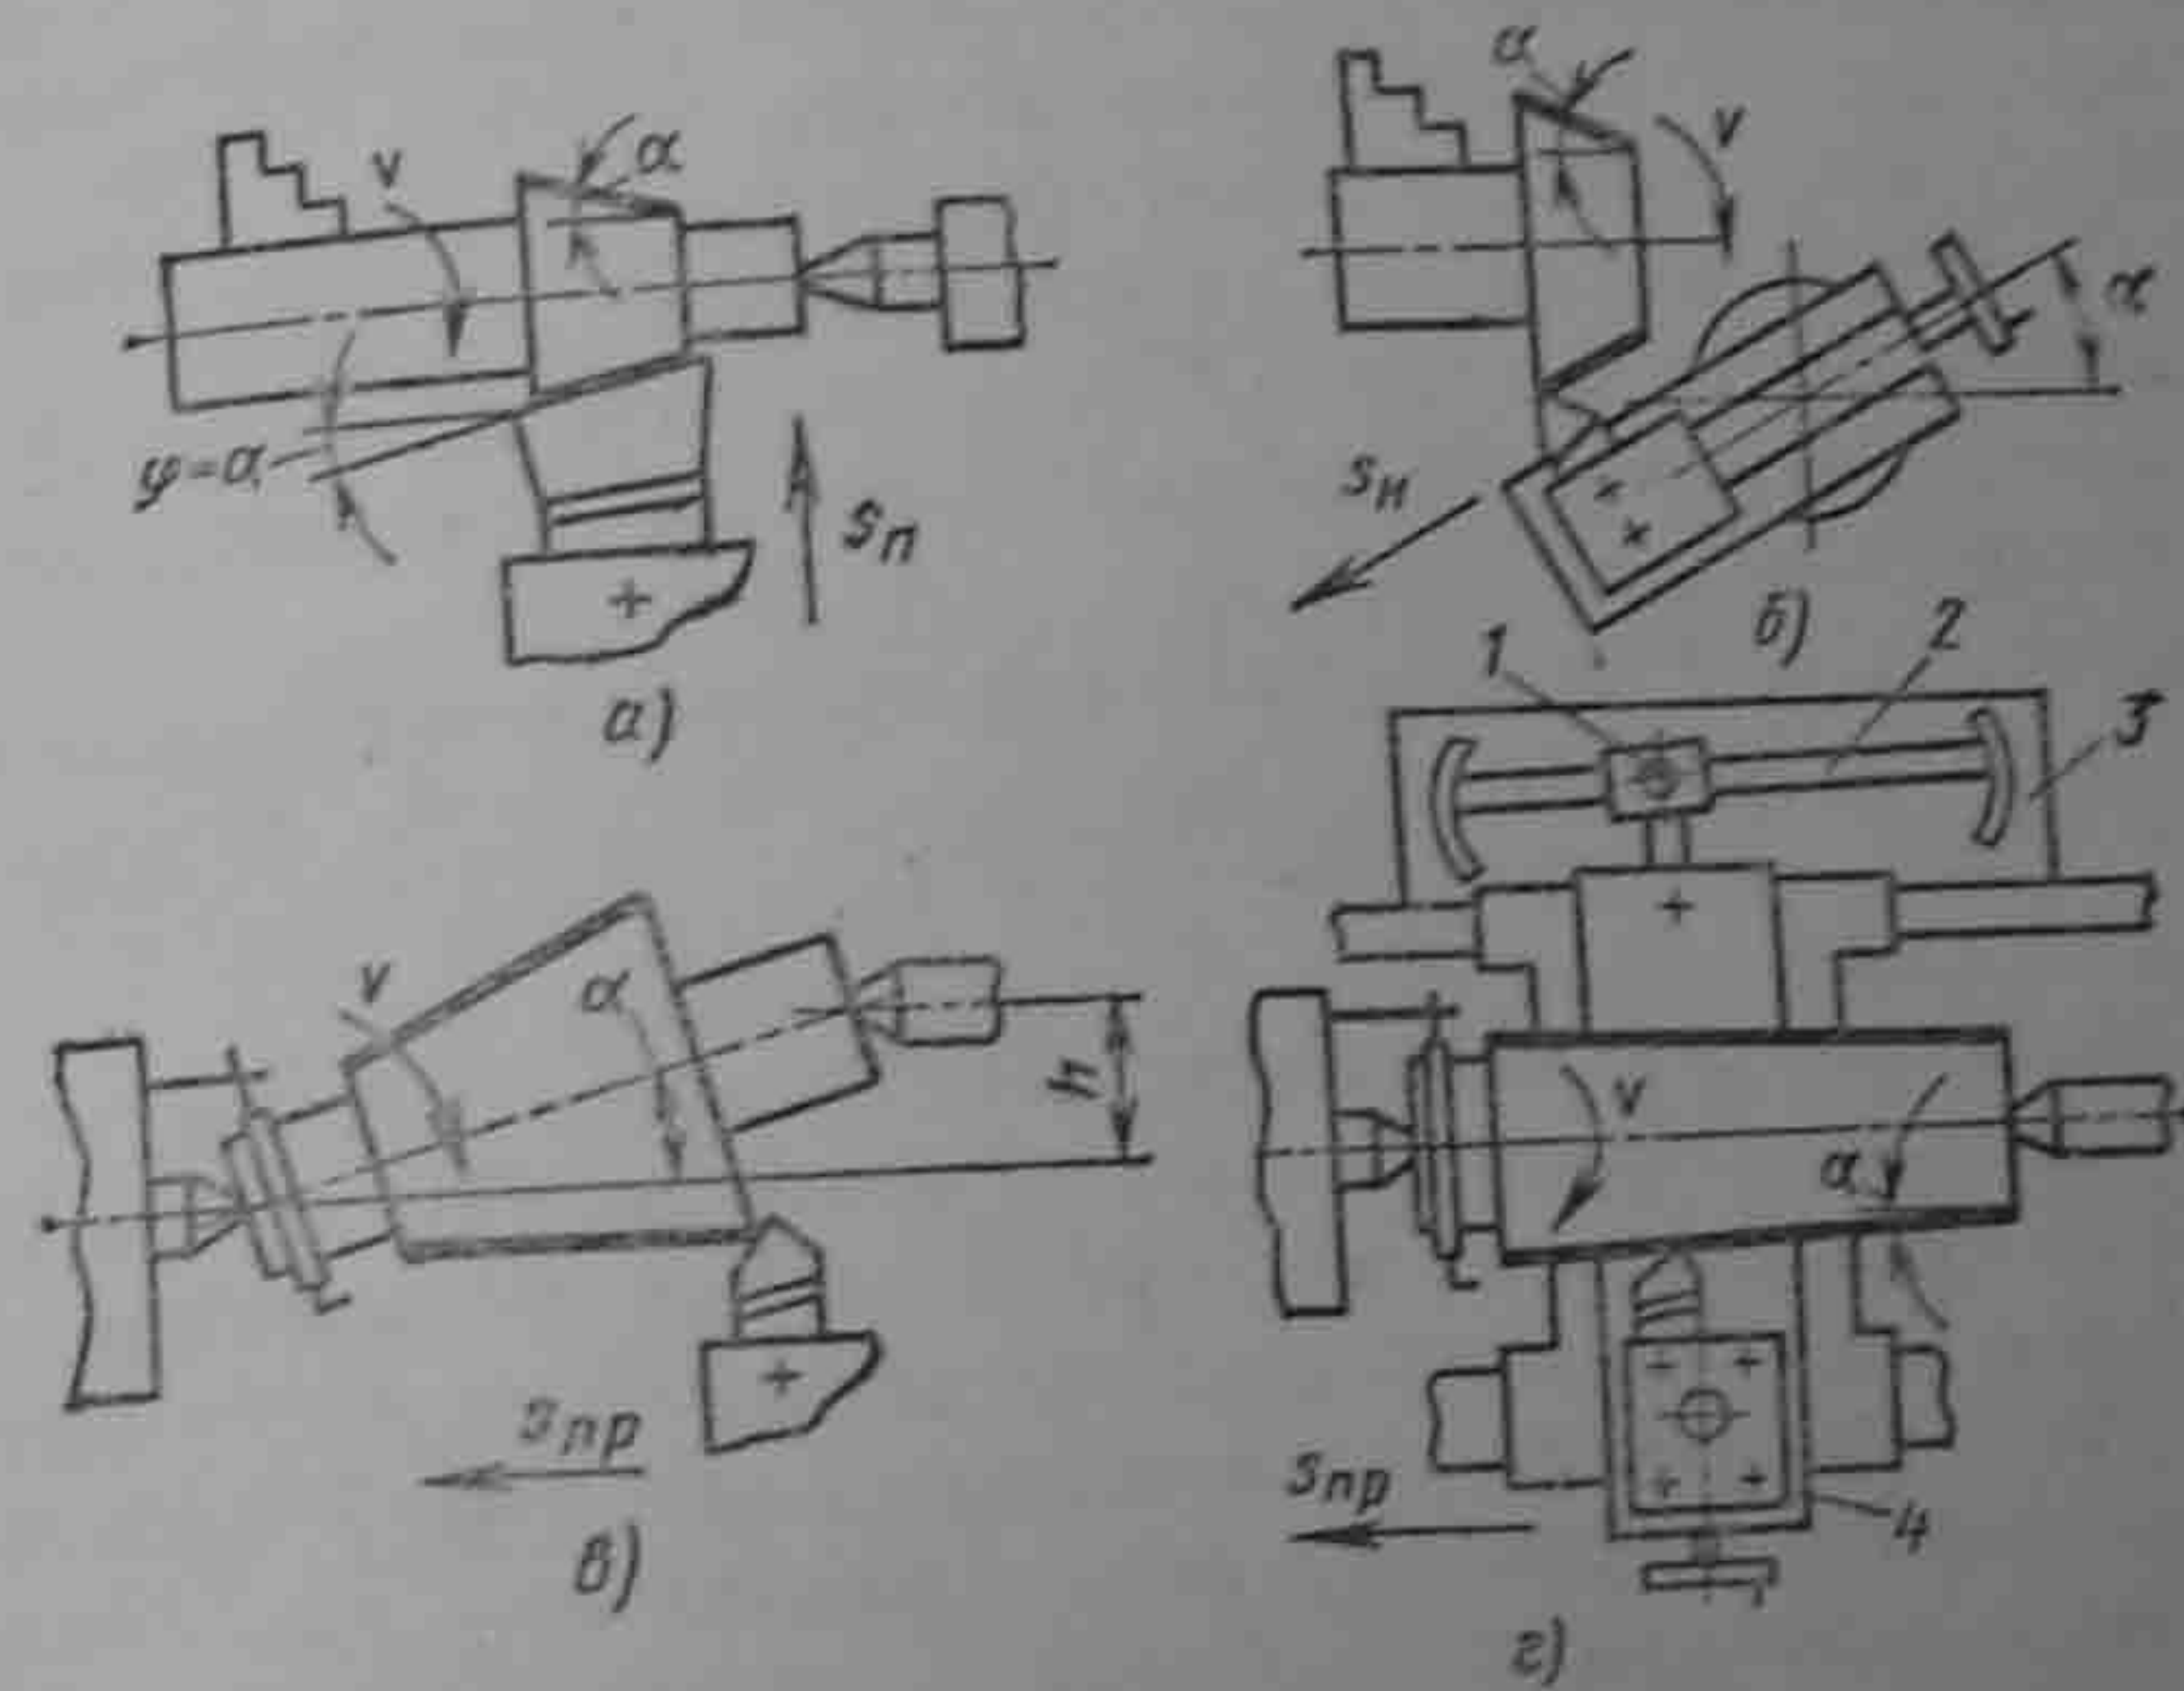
Схемы обтачивания наружных конических поверхностей на токарно-винторезном станке
